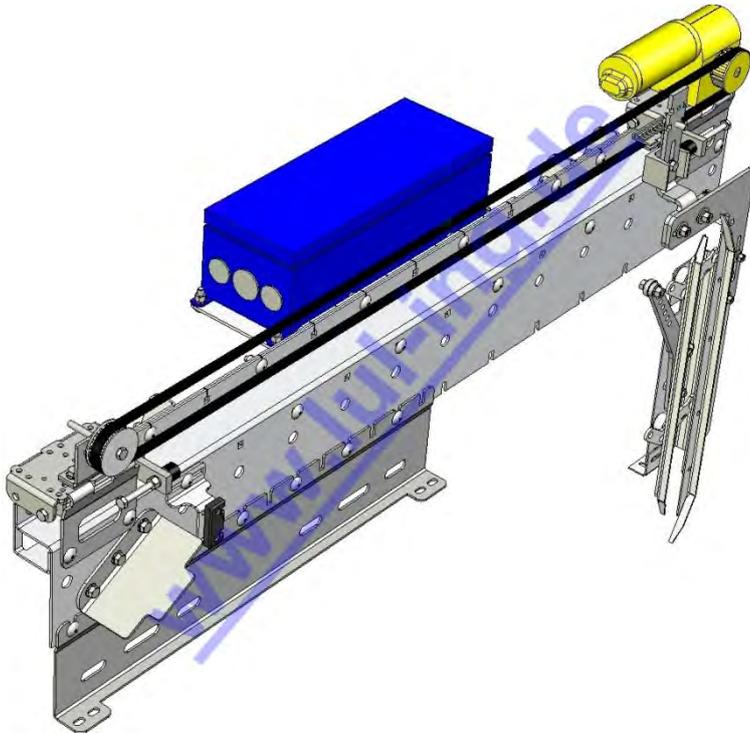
L&L QKS11 Türmaschine - 3D-Sicht (TR)
